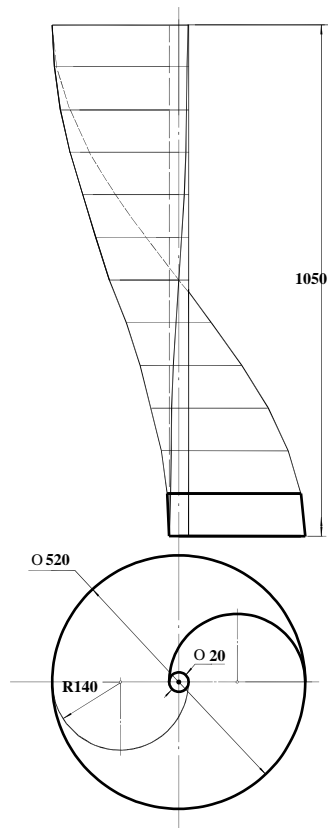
Етап підготовки вихідної схеми до наступного конструювання
